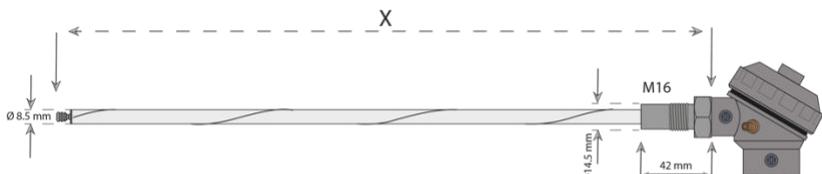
CarboProbe™ DS mit M16-Feingewinde
